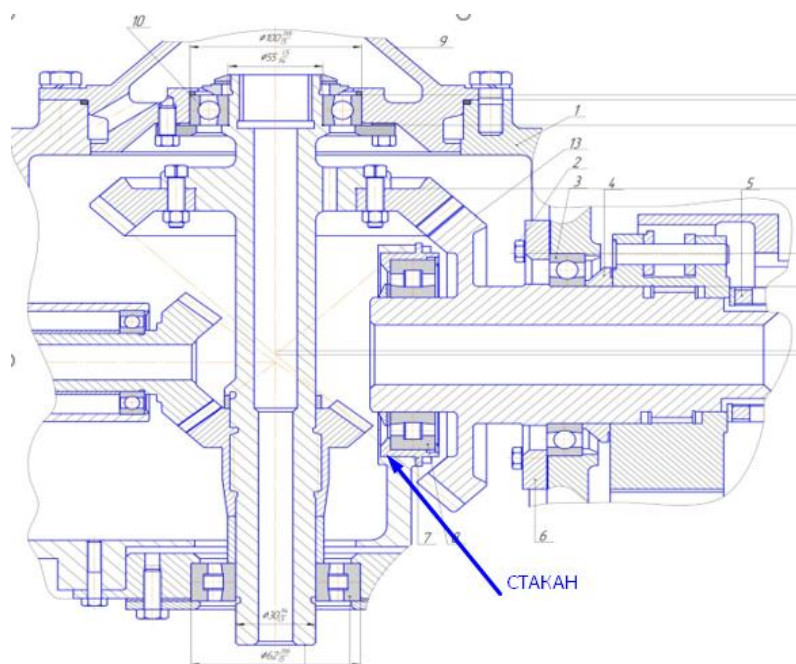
Складальний вузол коробки приводів:1-корпус,2- кришка, 3-підшипник кульковий А 116Л ЕТУ 100/3, 4-кільце, 5-ущільнююче кільце, 6-кільце, 7-СТАКАН, 8-Підшипник роликовий 6-32210Б ЕТУ 100/1, 9- кришка, 10- Підшипник роликовий 5-3220653 ЕТУ 100/3, 11-ресора
